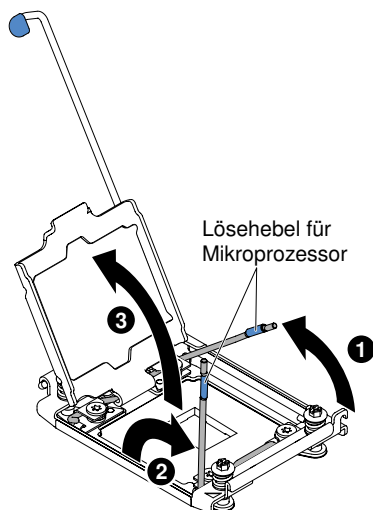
Hebel und Halterung des Mikroprozessorstecksockets lösen
